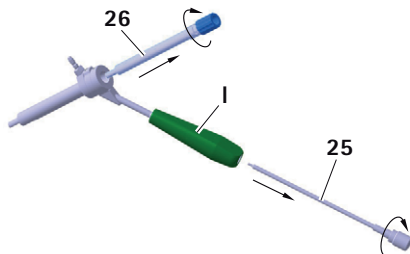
Demontage Führungshülse für Glattschaftschraube
